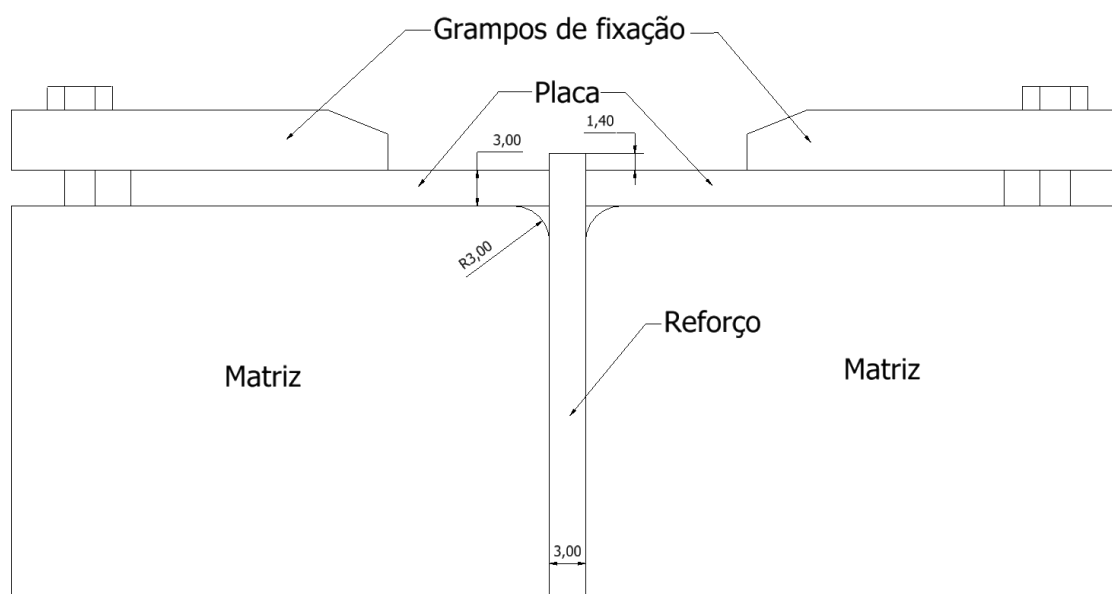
Configuração e fixação da junta T (medidas em mm).
